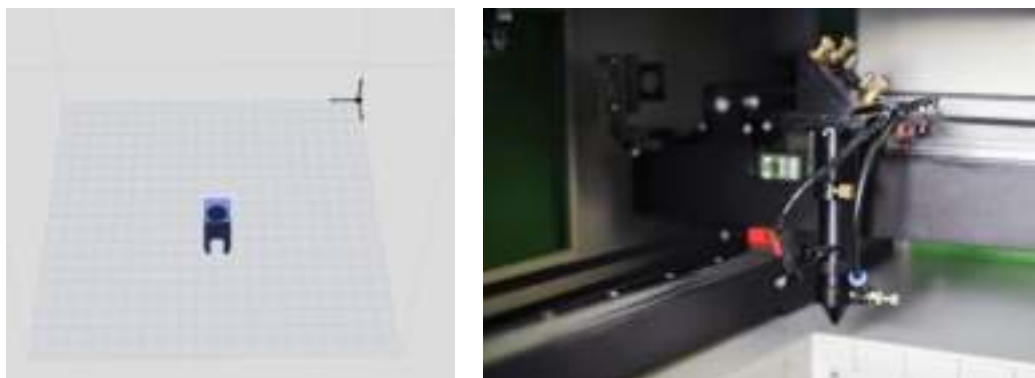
Прототип держателя полупроводникового лазера и сопло с креплением реального станка
